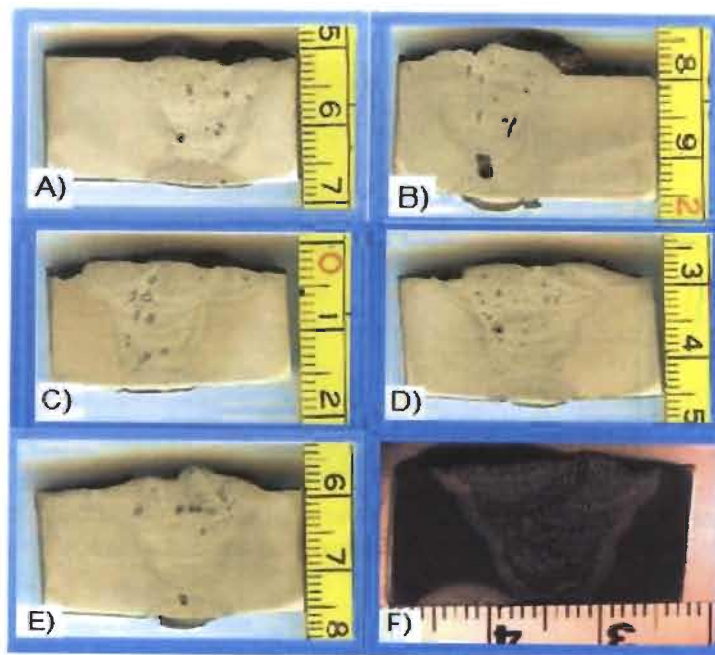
Aspecto general de los cupones de soldadura unidos a diferentes parámetros a) S4, b) S3 c) S2.
